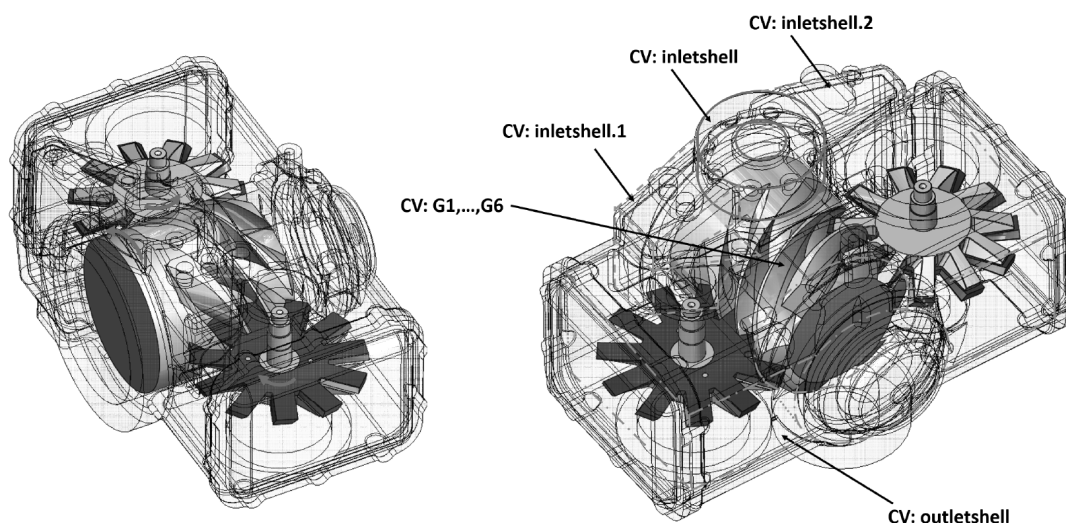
3-d изображение конструкции винтового однороторного компрессора
